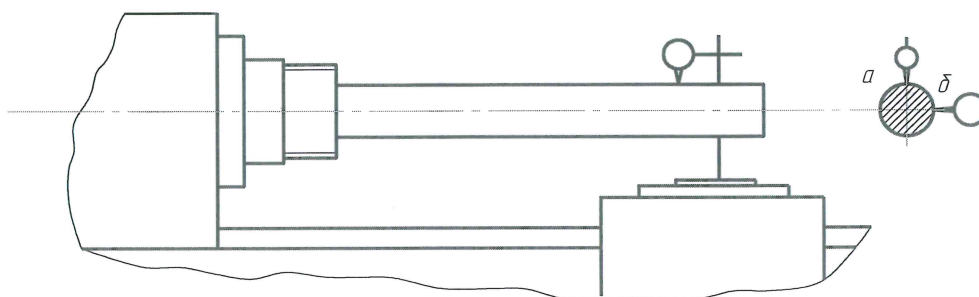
Схема установки индикатора для проверки параллельности оси шпинделя направлению продольного перемещения суппорта
